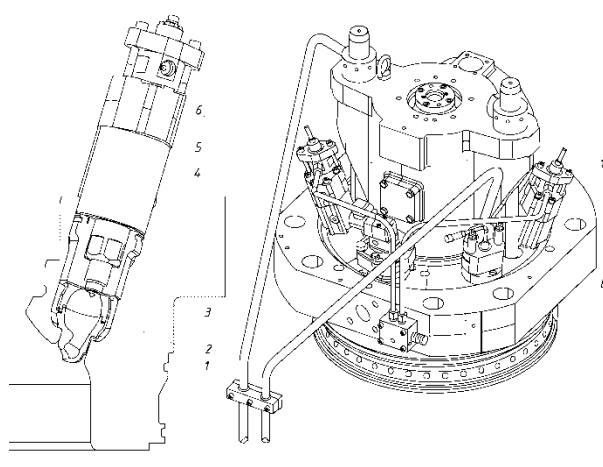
Модуль запального зажигания газо-воздушной смеси газодизельного двигателя RT-flexDF и его установка на крышке цилиндра: 1 – крышка цилиндра; 2 – вихрекамера; 3 – форсунка подачи запального топлива; 4 – воздушный клапан; 5 – форсунка подачи резервного ЖТ; 6 – запальный модуль; 7 – корпус выпускного клапана; 8 – коллектор подвода запального топлива
